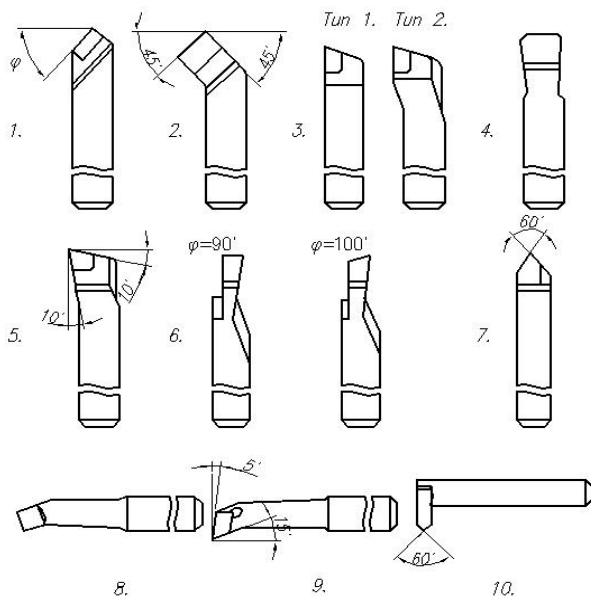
Резцы токарные с пластинкой из твердого сплава.
